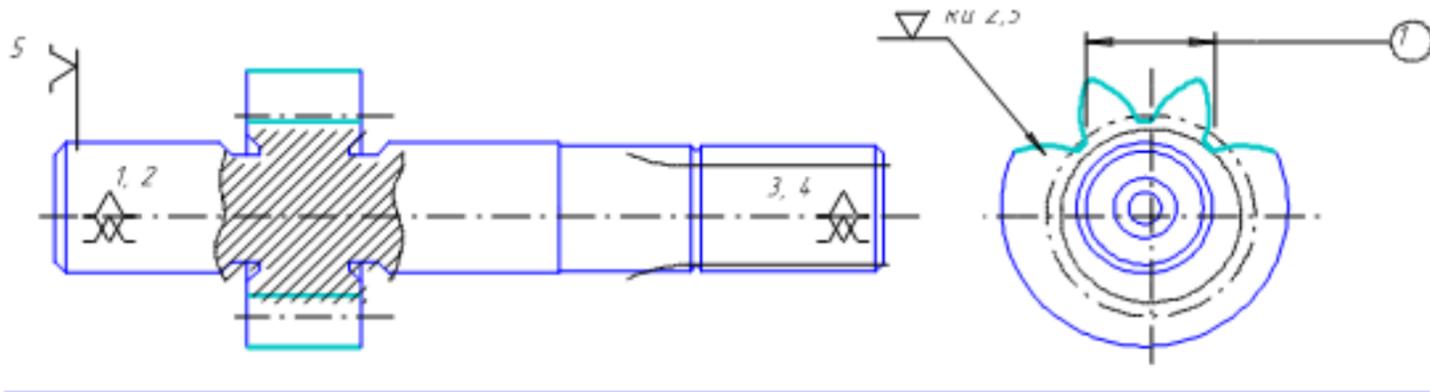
Схема базування та обробки на зубошевінгувальній операції
